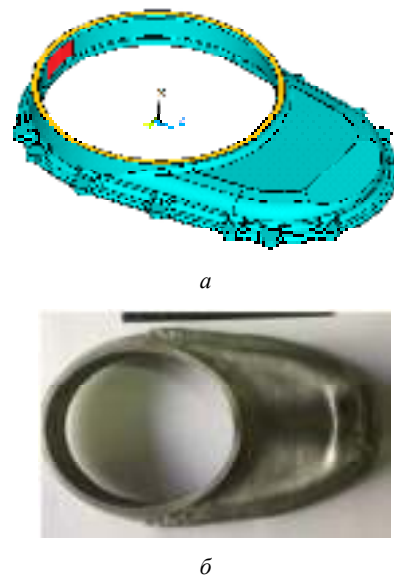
Деталь «Крышка редуктора»: а – упрощенная твердотельная модель крышки с указанием поверхностей приложения нагрузок, б – выращенная деталь Крышка редуктора из алюминиевого сплава
